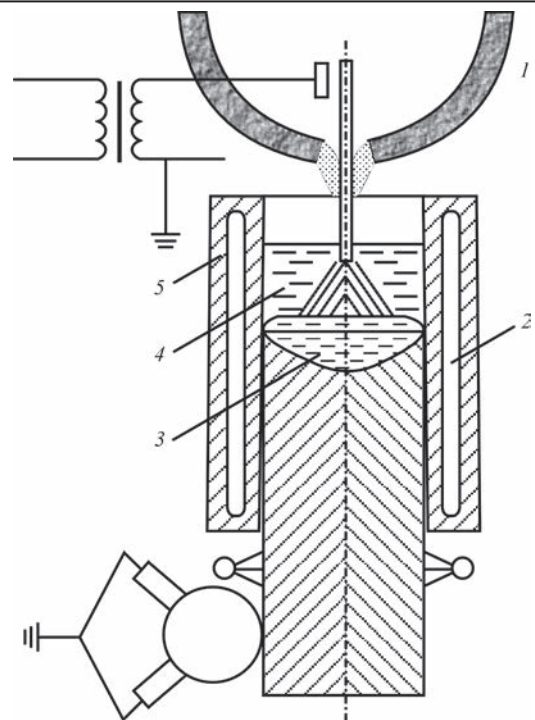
Схема процесса НЭШП: 1 — питатель порошка; 2 — водяное охлаждение; 3 — жидкий металл; 4 — шлаковая ванна; 5 — кристаллизатор
